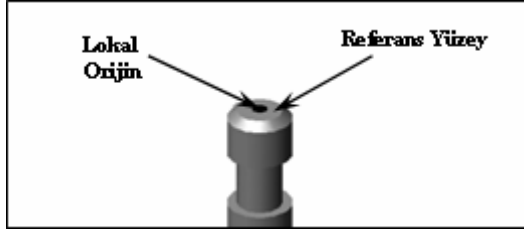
M8x50 flanşlı civatanın tanıma işlemi (Recognition process of M8x50 flanged bolt)
